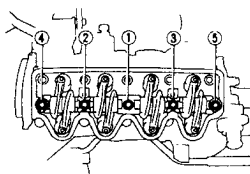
Порядок затяжки болтов крепления оси коромысел (См. Раздел 17)
